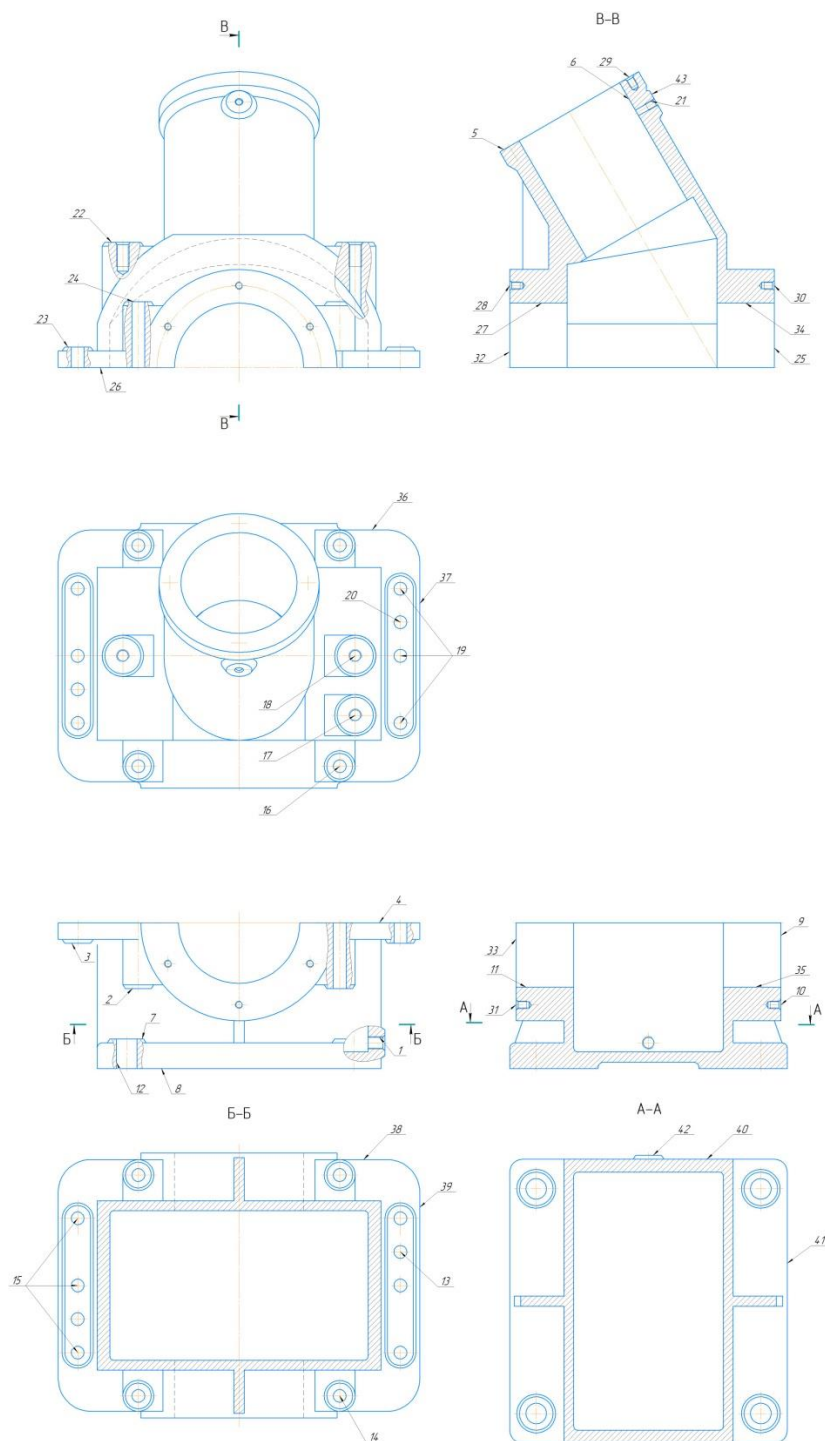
Технологический эскиз детали «Корпус конического редуктора»
